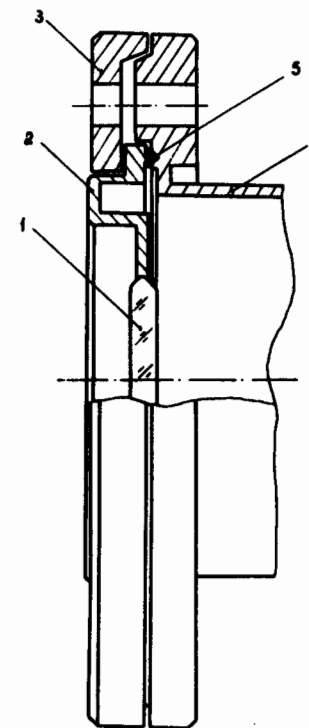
Конструкция окна: 1 - диск из оптической керамики КО-1; 2 - оправка с тонкостенным разгрузочным гофром; 3 - прижимный фланец; 4 - патрубок вывода синхротронного излучения; 5 - уплотнительная металлическая прокладка.
